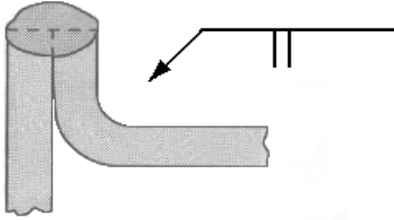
Soldadura de borde para lámina de metal y cargas ligeras.
